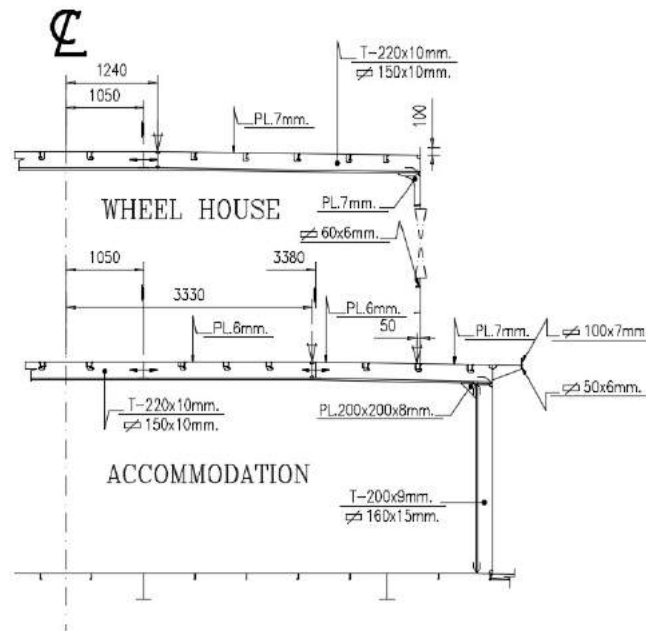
Estructura longitudinal tipo. Fuente: SENER
